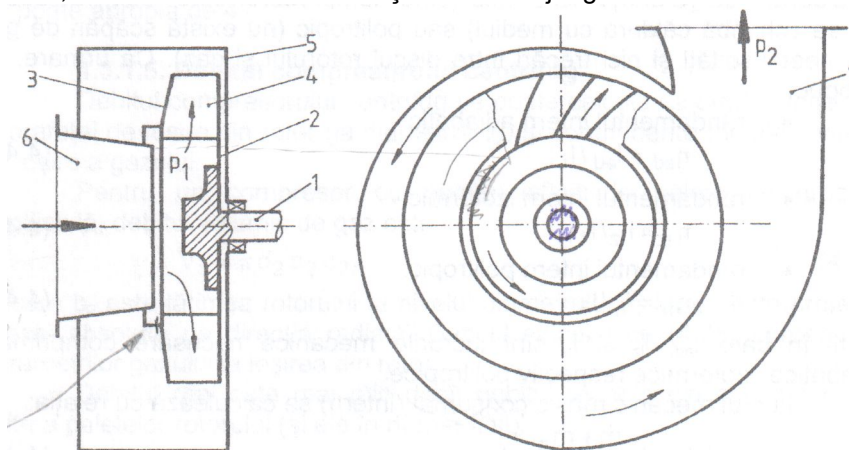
Ventilator centrifug: 1 - arbore; 2 - disc; 3 - capac; 4 - palete; 5 - carcasă; 6 - gură de aspirație; 7 - gură de refulare
